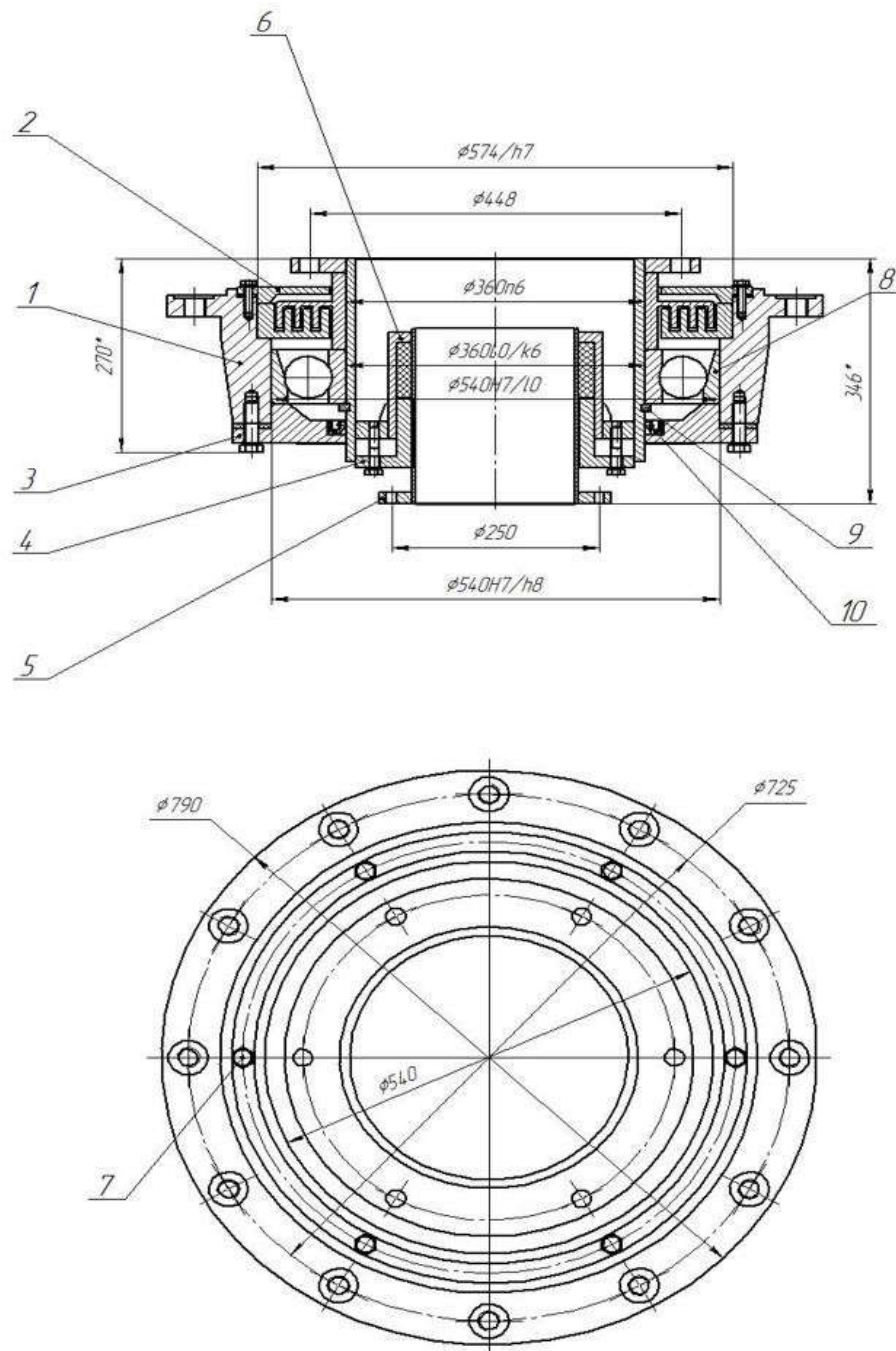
Нижня опора трубовала вертикального перемішувача-кристалізатора
